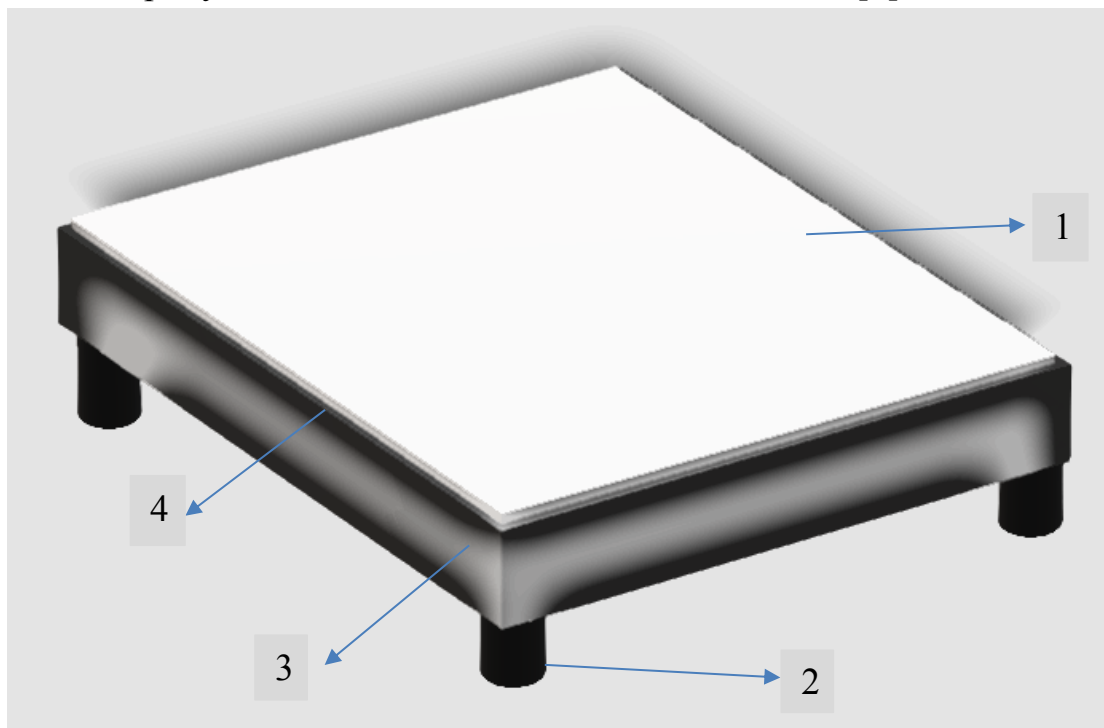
Конструкция изготовленной поверочной плиты:
